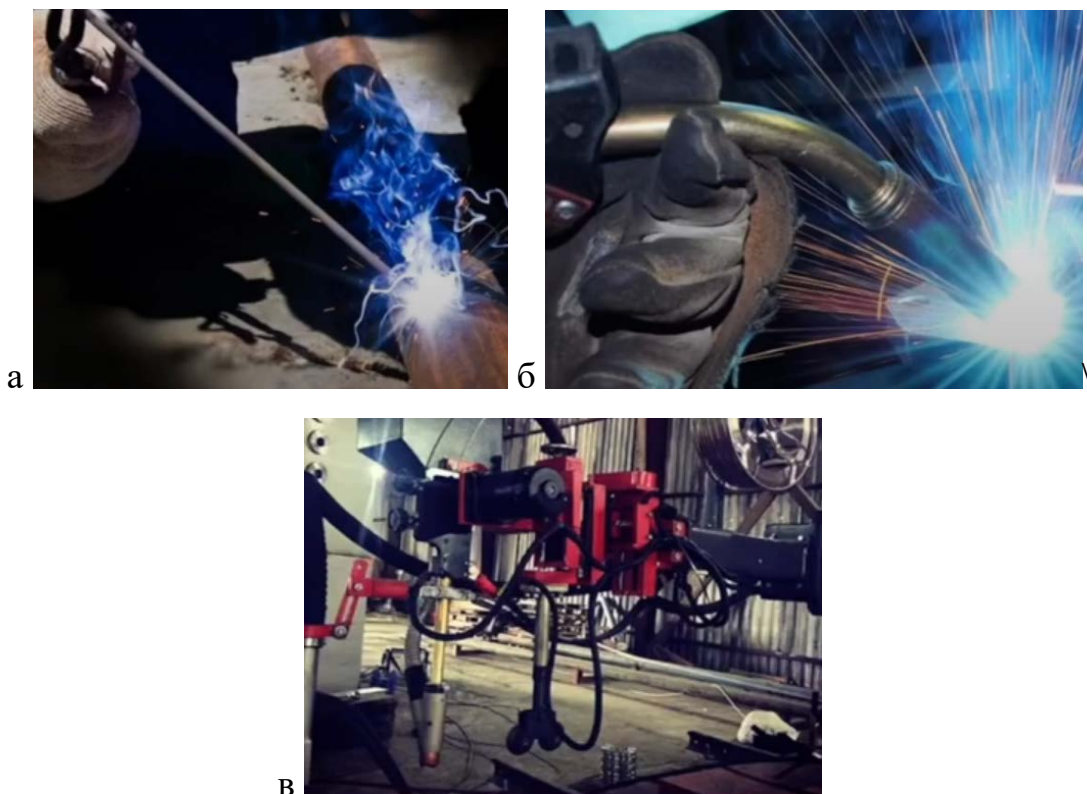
Ручне зварювання (а), механічне (напівавтоматичне) зварювання (б), автоматичне зварювання (в)
